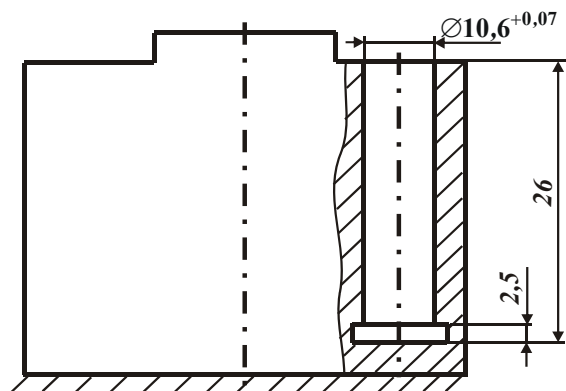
Схема расположения глухого отверстия в блоке цилиндров.
